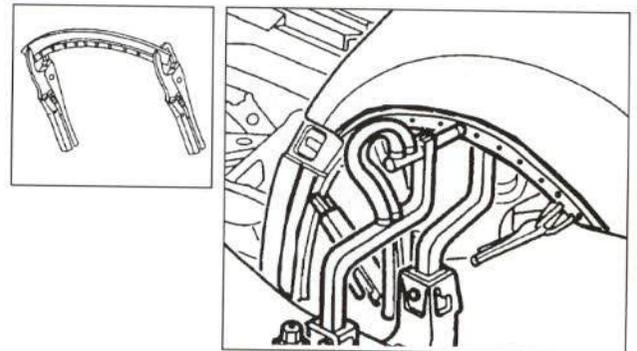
Placa de cobre entre la aleta y el electrodo.
